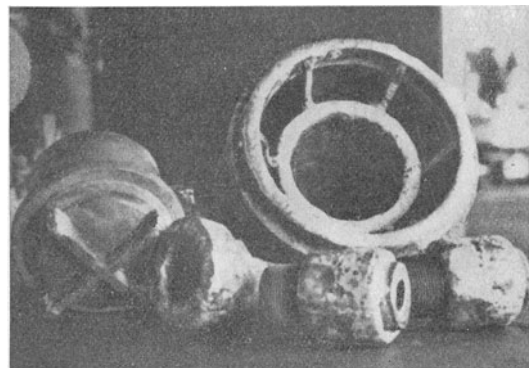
Einzelteile abgenutzter Dampfventile aus Bronze. Aufgetragen mit BG
